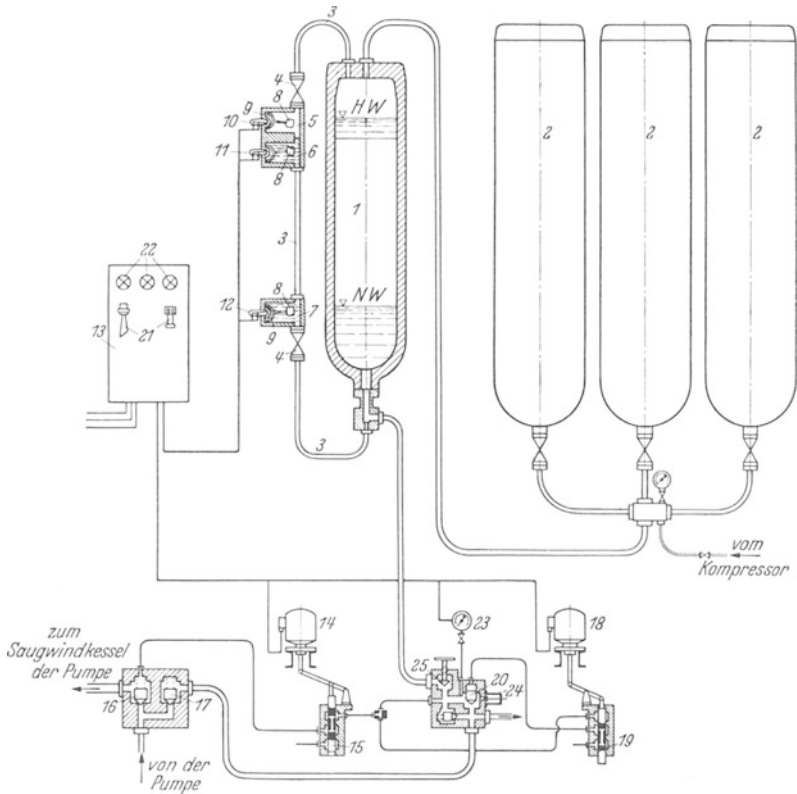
Steuerschema für einen Druckluftakkumulator mit elektrischen Kippschaltern.
